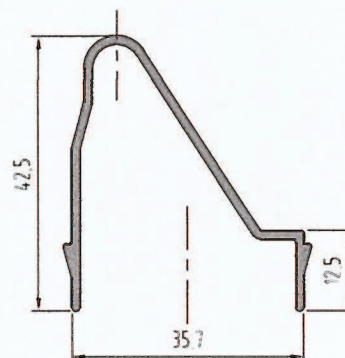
Przekrój poprzeczny: poprzeczka profil TS02
